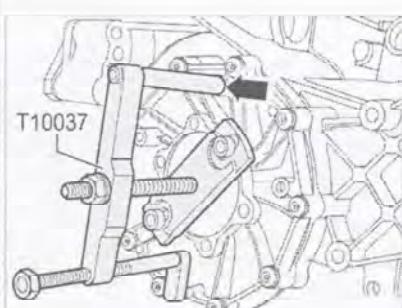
Закрепите на крышке главной передачи съемник T10037 (стрелка) и снимите левый приводной вал.
